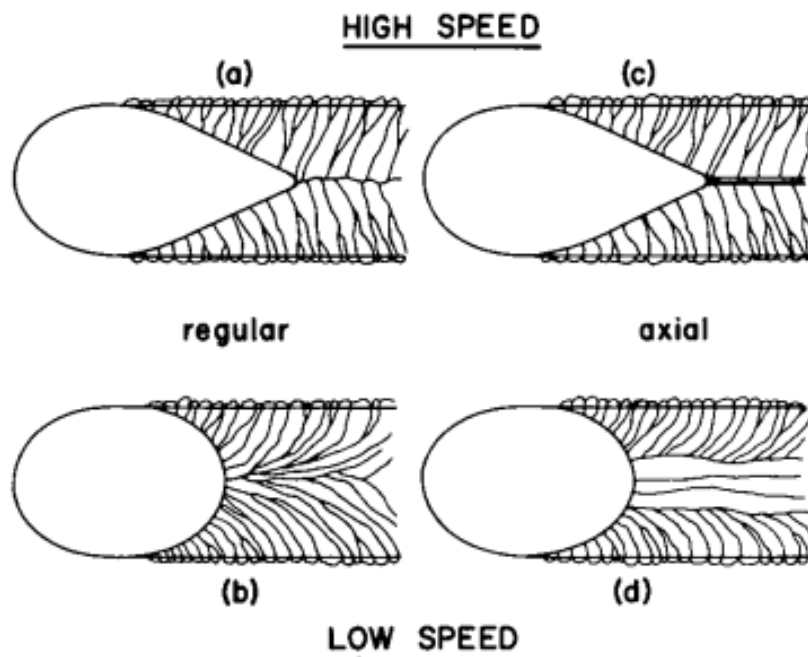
Effet de la vitesse de soudage sur la structure dans le métal soudé [27]
